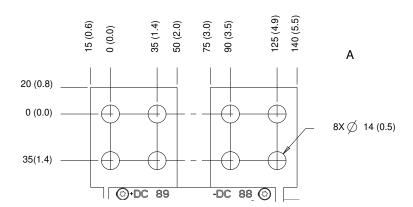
Dimensions des bornes de répartition de la charge/régén. E4h (vues latérales)
